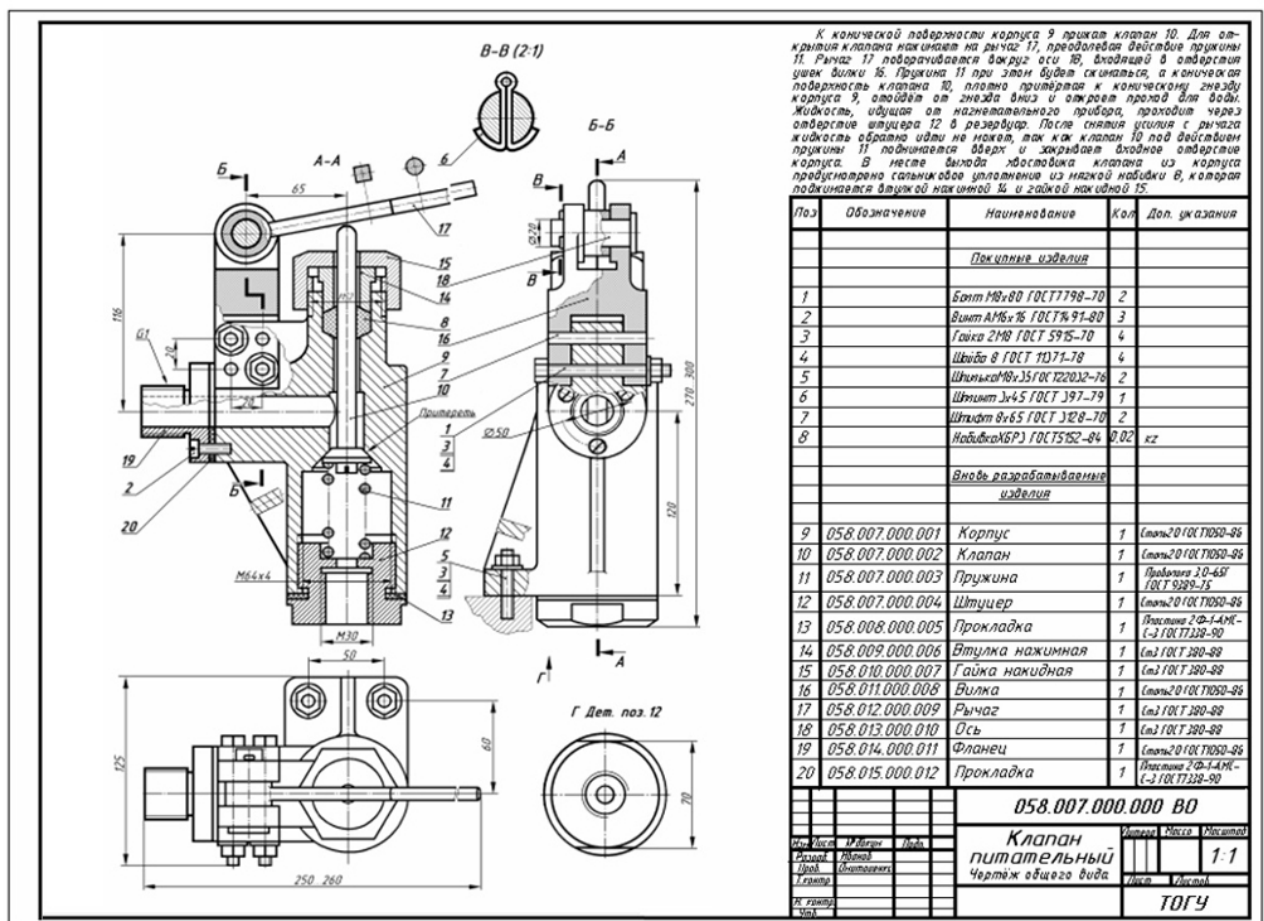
Чертеж общего вида сборочной единицы «Клапан питательный»
